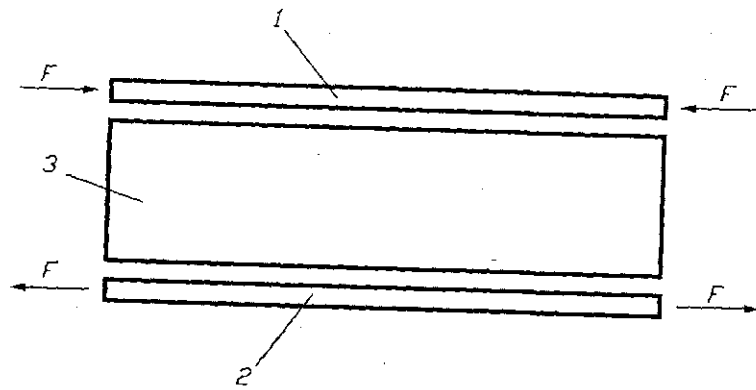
Упругое деформирование полок сварного двутавра перед сваркой: 1 — верхняя полка; 2 — нижняя полка; 3 — стенка двутавра
